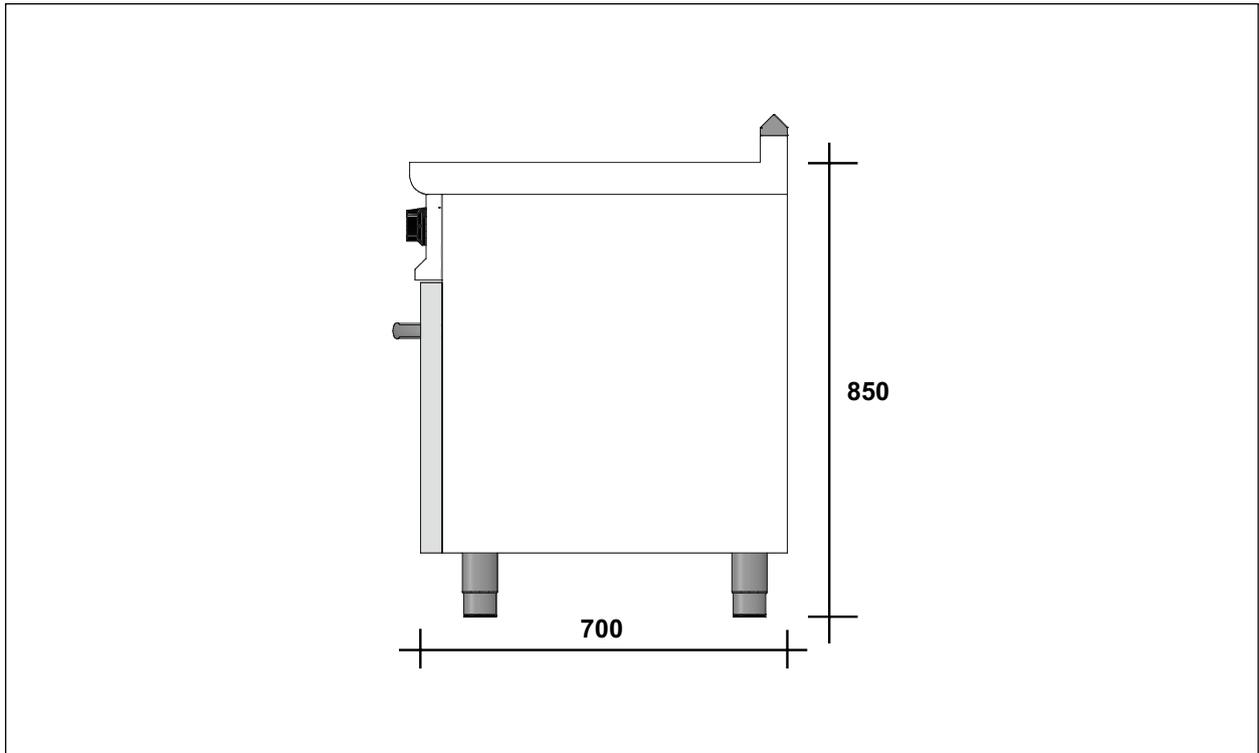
Dimensions de la cuisinière plan en vitrocéramique
